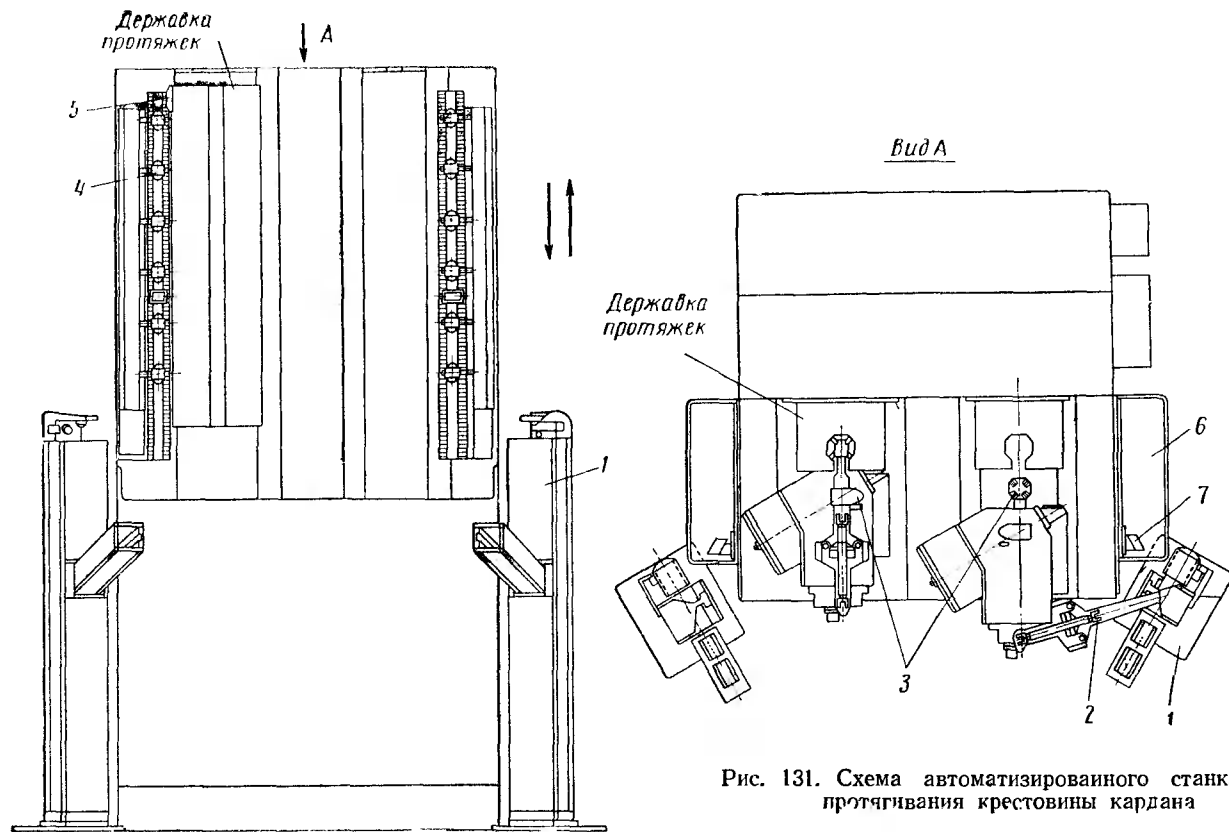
Схема автоматизированного станка для протягивания крестовины кардана
